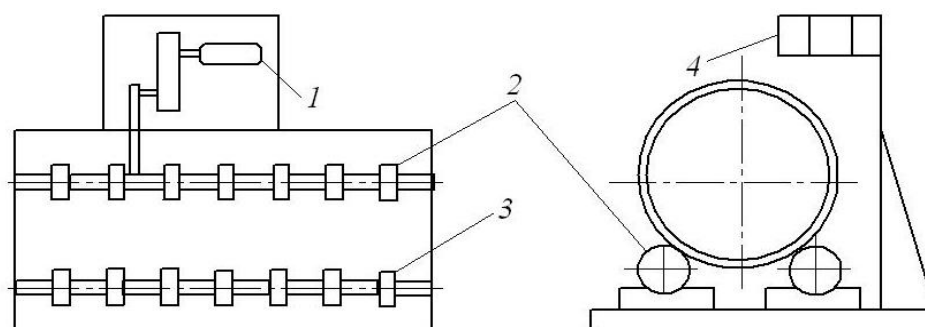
Пристрій автоматичного зварювання колонних апаратів
